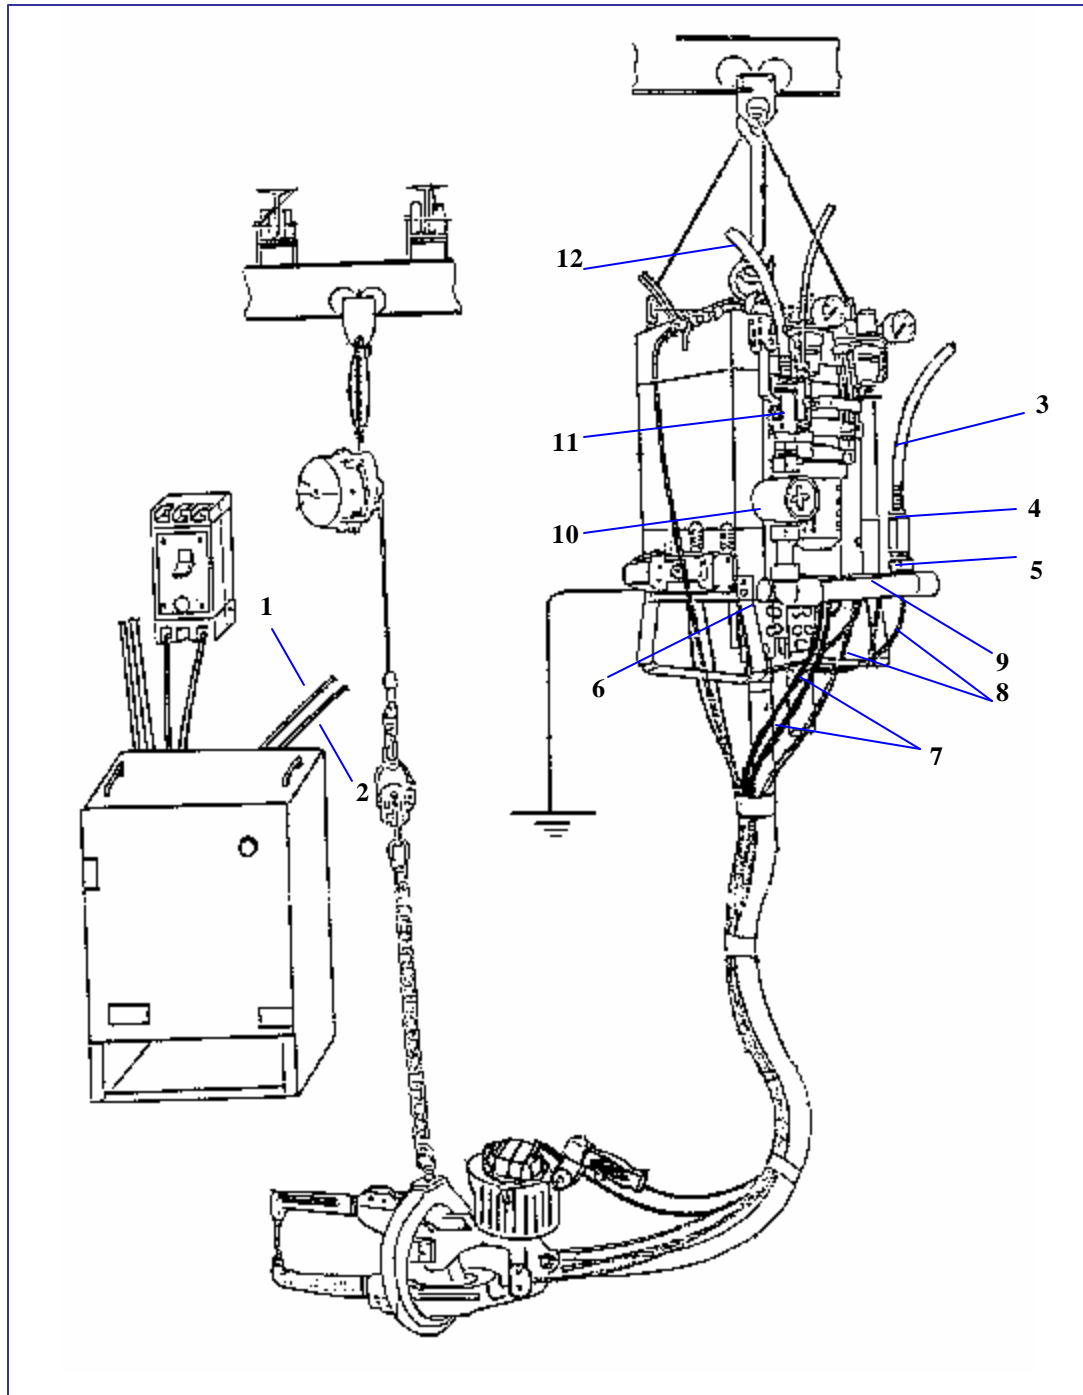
Partes del sistema de enfriamiento de un equipo soldador de puntos
